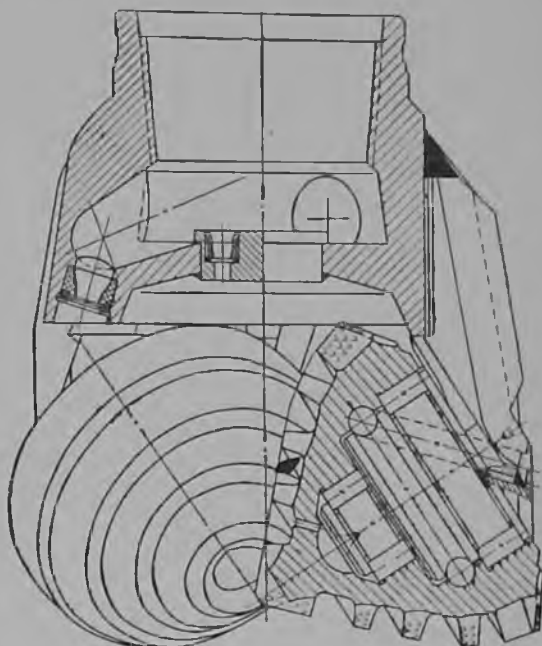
Гидромониторное корпусное долото с литым корпусом.
